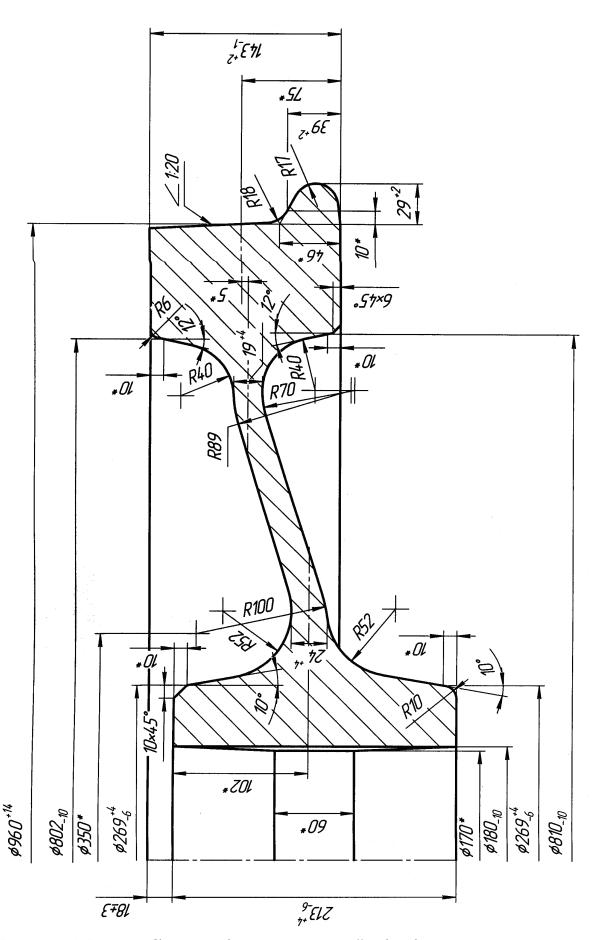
Колесо Ø960 мм без механической обработки, для Ø957 мм по чертежу № КР-0048-15. Масса колеса 456кг
